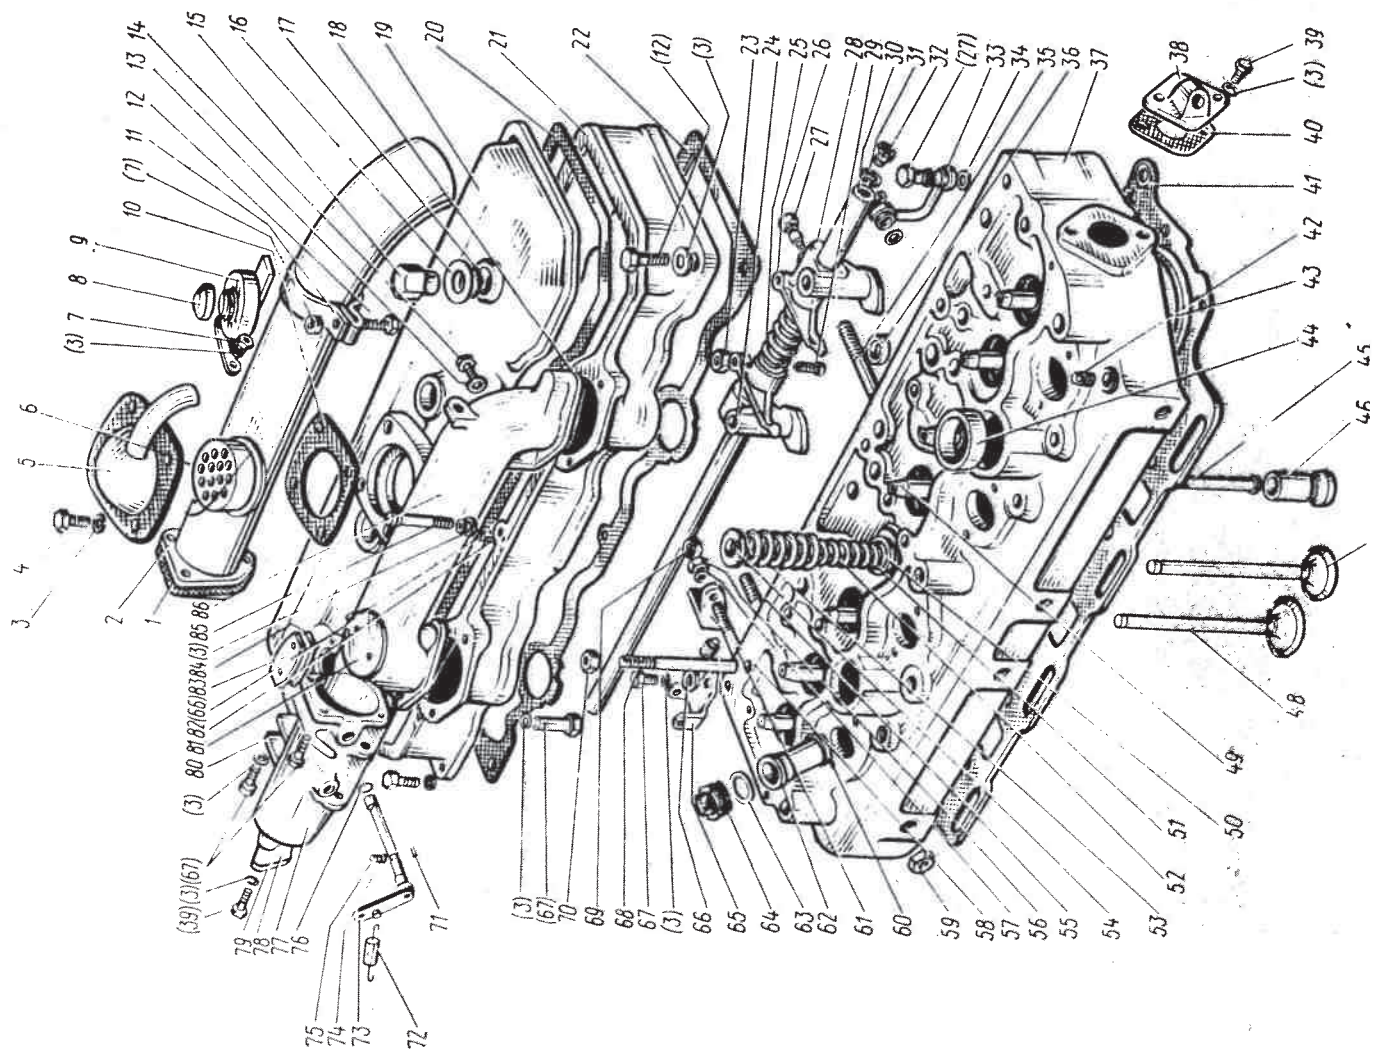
Головка цилиндра. Клапаны и толкатели клапанов
